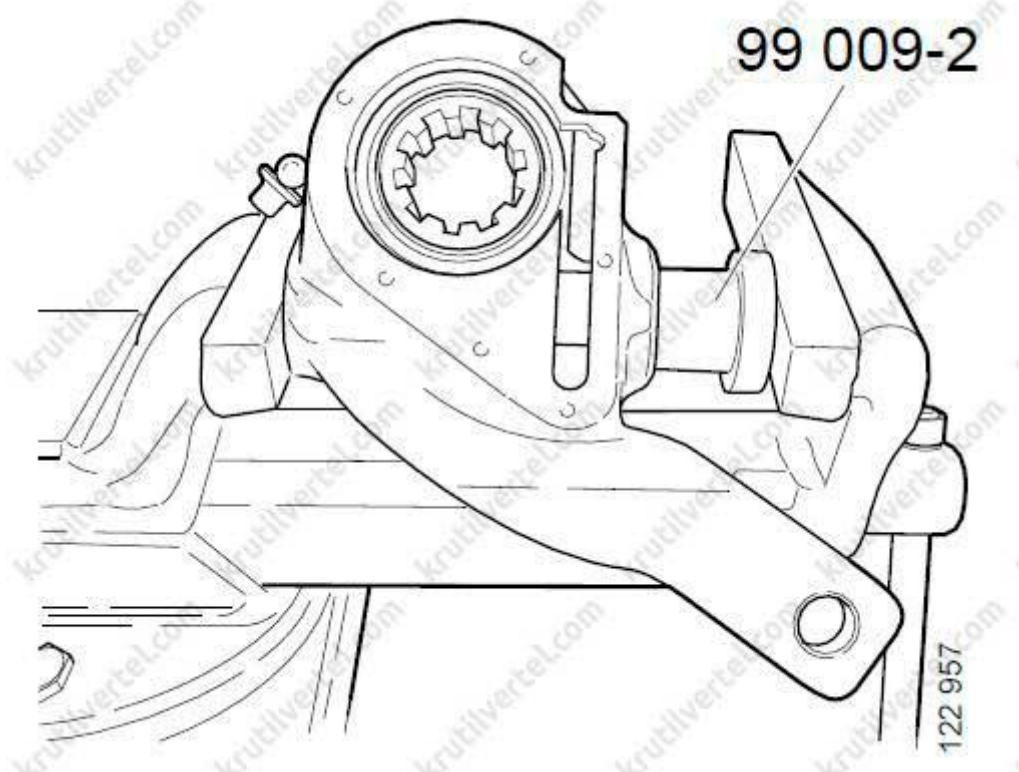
Напресування втулки підшипника оправленням 99009-2
